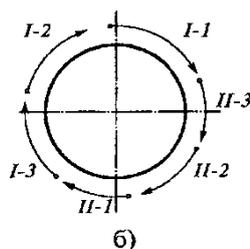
Порядок наложения корневого шва горизонтального стыка при сварке двумя сварщиками
